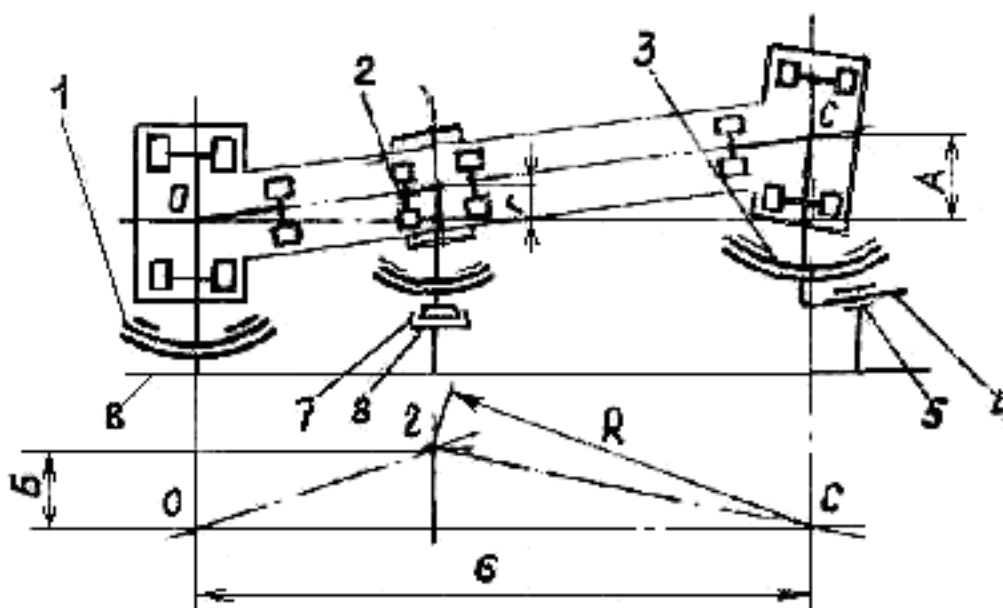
Схема установки заготовки по трем скрытым базам – точкам
